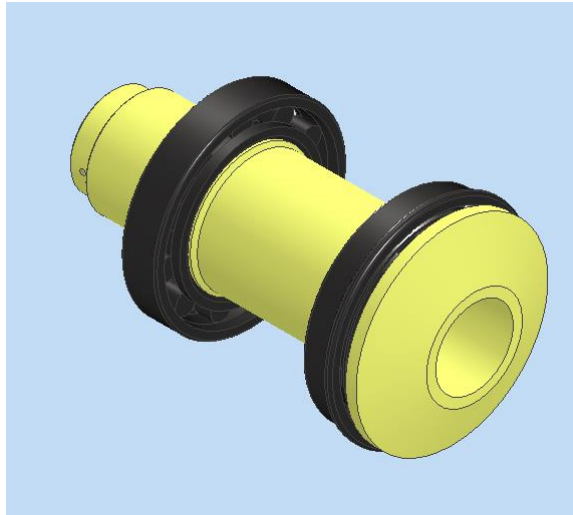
Шпиндель ділильної головки із підшипниками
